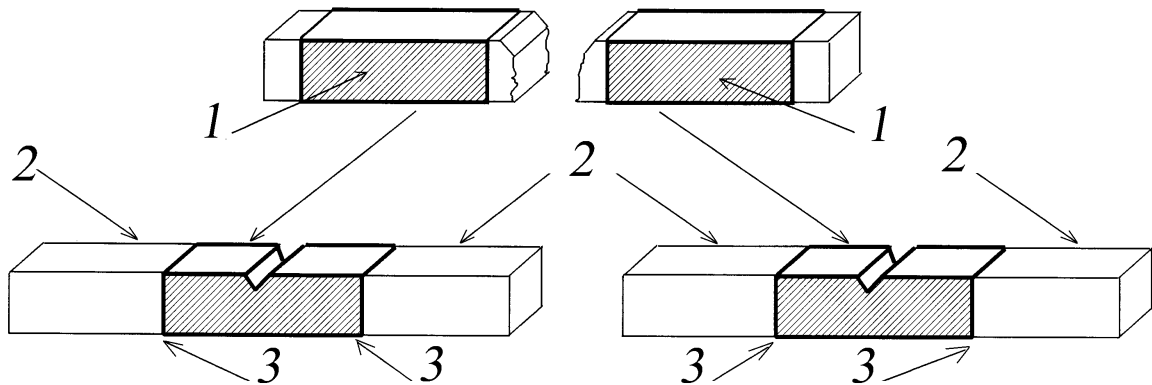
Схема реконструкції зразків Шарпі: 1 – вставки, виготовлені з половинок зразків-свідків типу «Ш» або «С»; 2 – хвостовики; 3 – зварні шви
